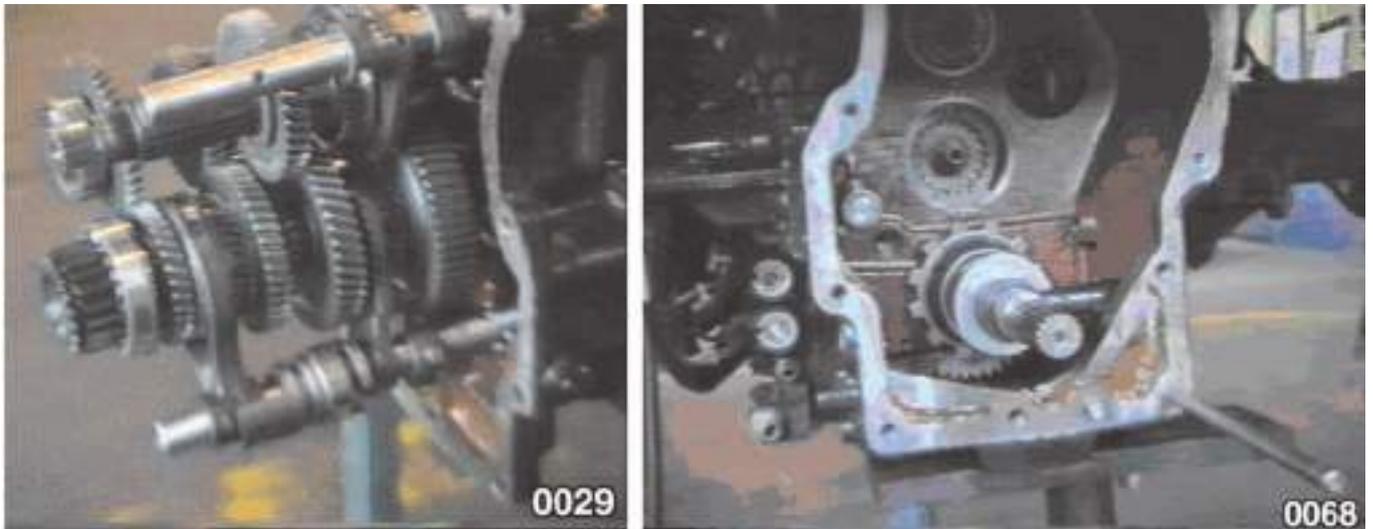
Désaccouplement du carter de boîte avant de la boîte arrière.
